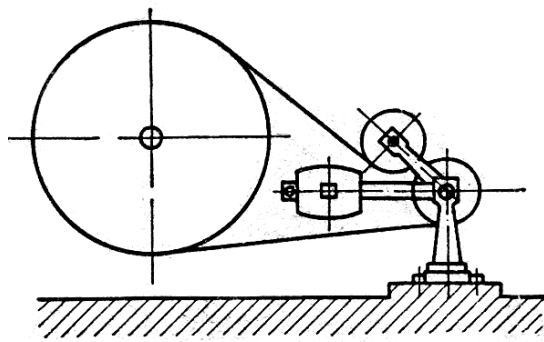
Схема ременной передачи с натяжным роликом:
